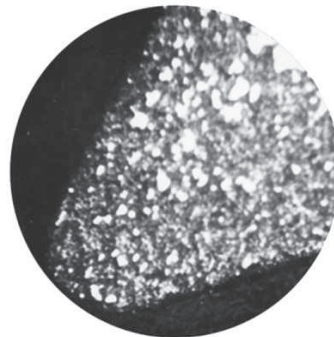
Схема износа резца из стали P18 с твердостью HRC = 62
